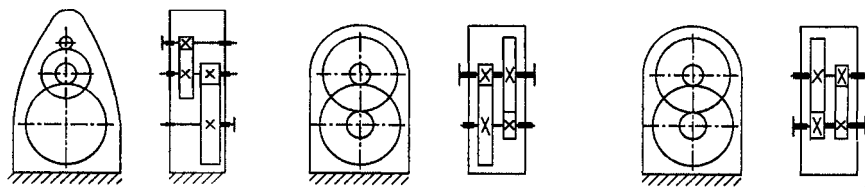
Цилиндрические двухступенчатые вертикальные редукторы
